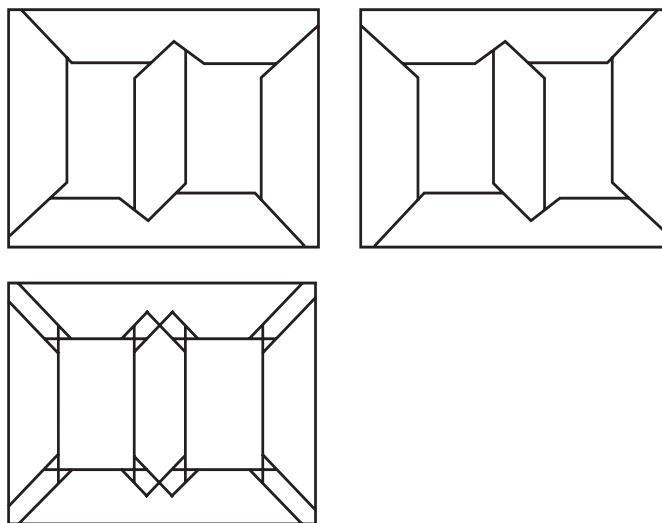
Стыковка стальных пластин под углом 45° и шихтовка по технологии Step-Lap
